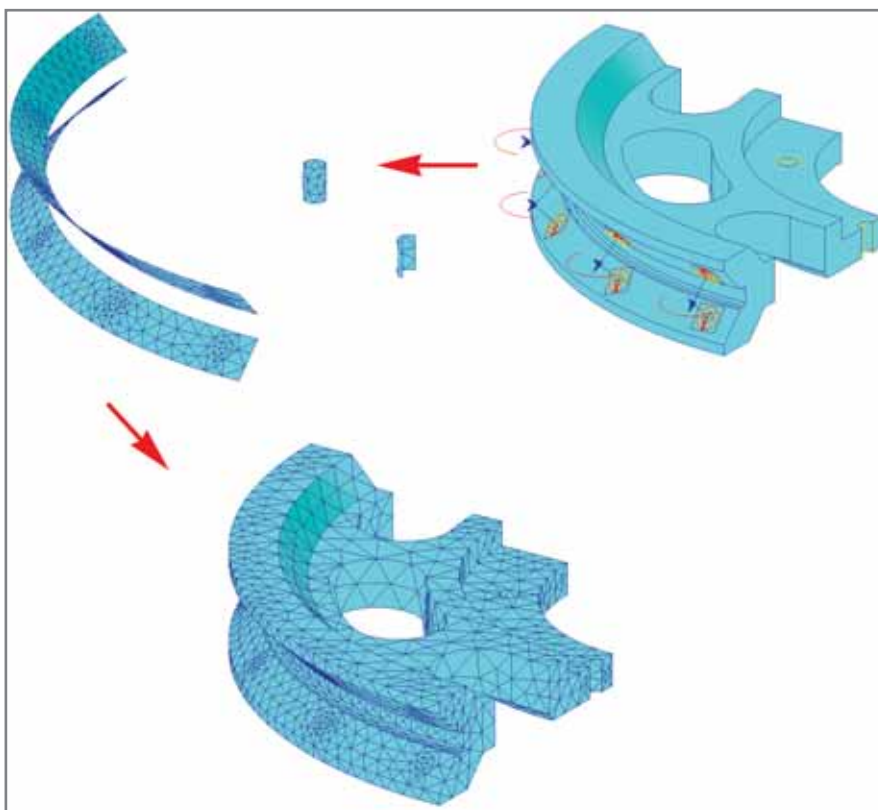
Формирование КЭ-сетки для внутреннего кольца подшипника
